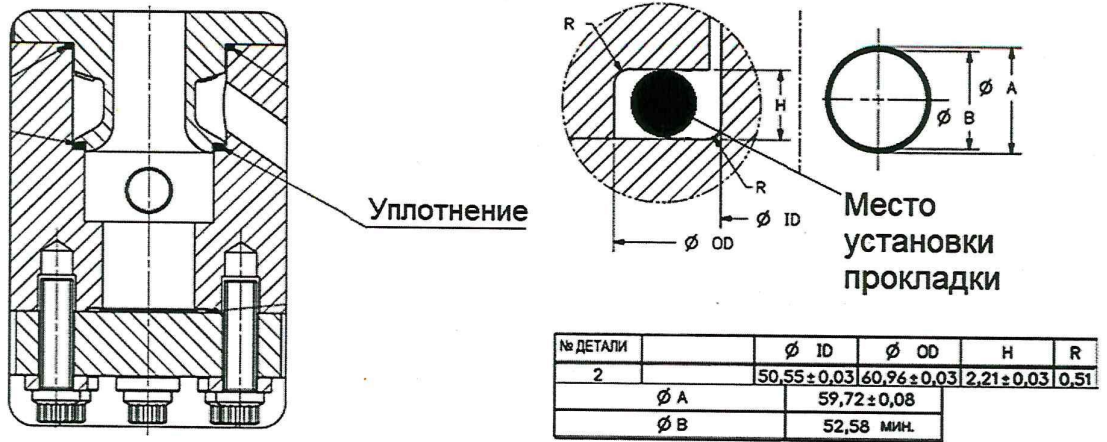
Схема расположения и общие габариты места установки уплотнения неподвижного
